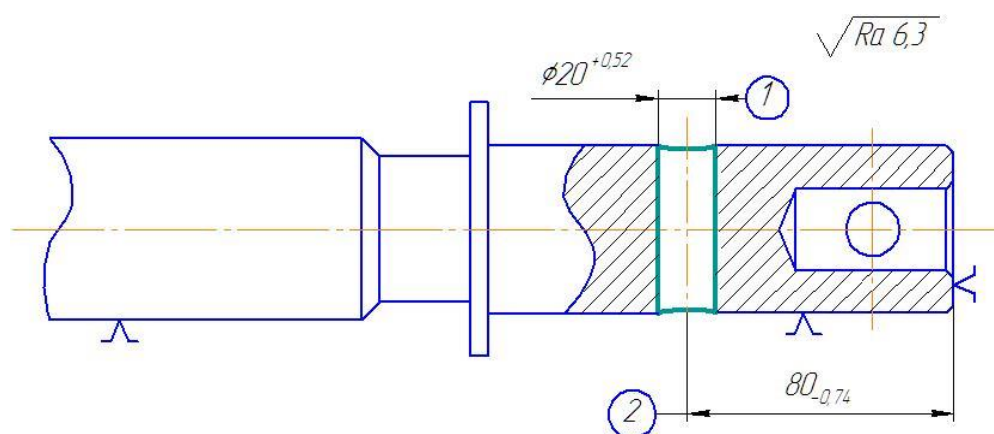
Закріплення заготовки в призмах при виконанні свердильних операцій
